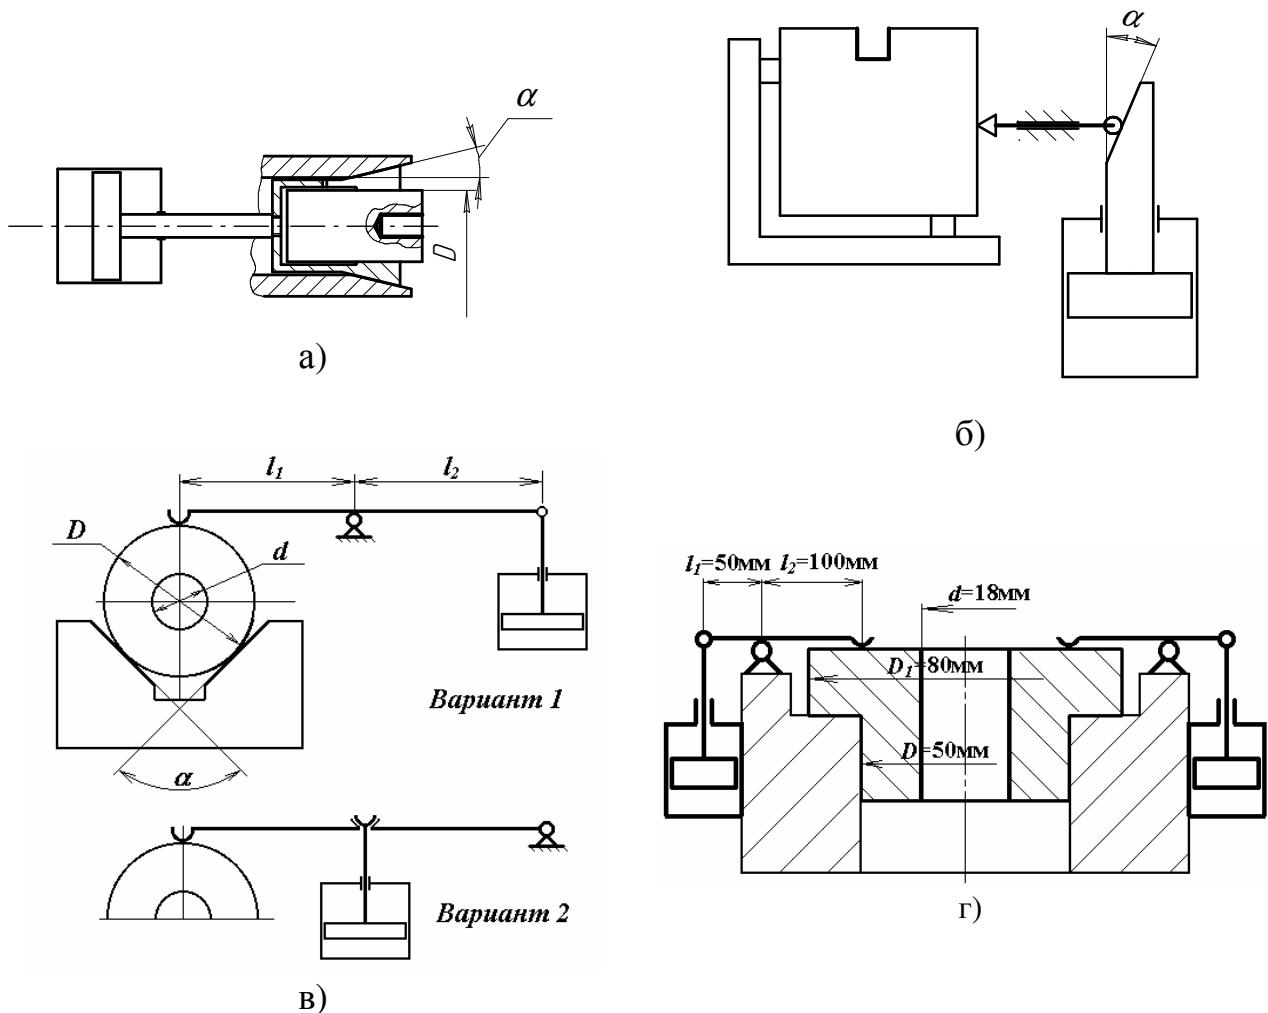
Принципиальные схемы приспособлений (а – с цанговым зажимным механизмом; б) с клиноплунжерным зажимным механизмом; в,г- с рычажными зажимными механизмами)
